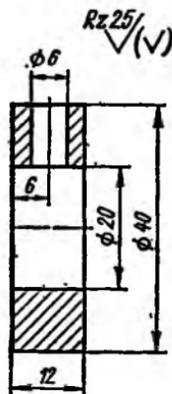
Габариты рабочего пространства устройства для поперечного сверления
